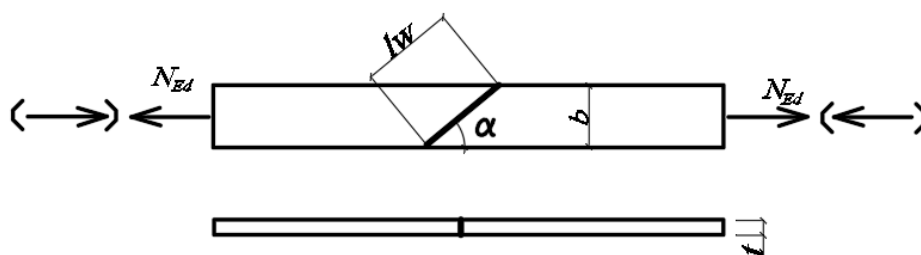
Косой стыковой сварной шов
